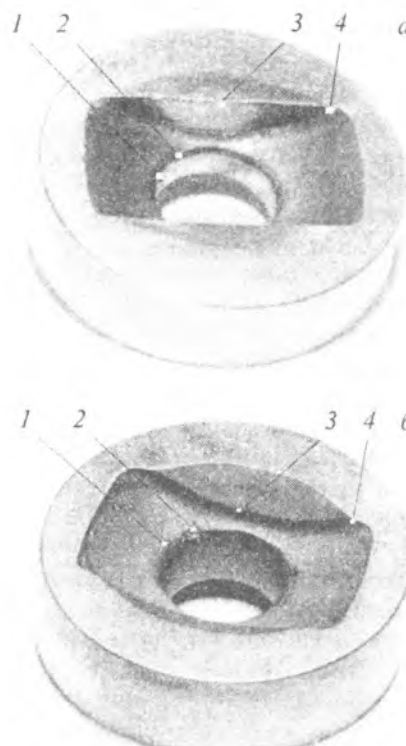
Холодновысадочная матрица: а – без разгружающих камер; б – с разгружающими камерами; 1–4 – точки максимальных напряжений, действующих на рабочую поверхность
